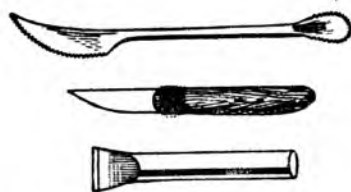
Долото, нож и лопатки с зубцами для формовки
